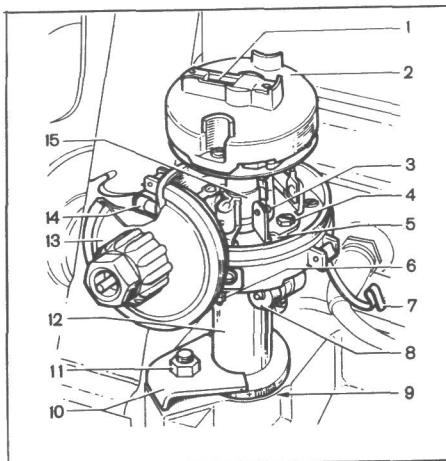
Распределитель зажигания: 1 — мехоподавляющее сопротивление; 2 — бегунок; 3 — контакты прерывателя; 4 — винт; 5 — паз; 6 — клемма; 7 — пружинная защелка; 8 — конденсатор; 9 — шкала; 10 — кронштейн; 11 — гайка; 12 — корпус; 13 — вакуумный корректор; 14 — масленка; 15 — кулачок
